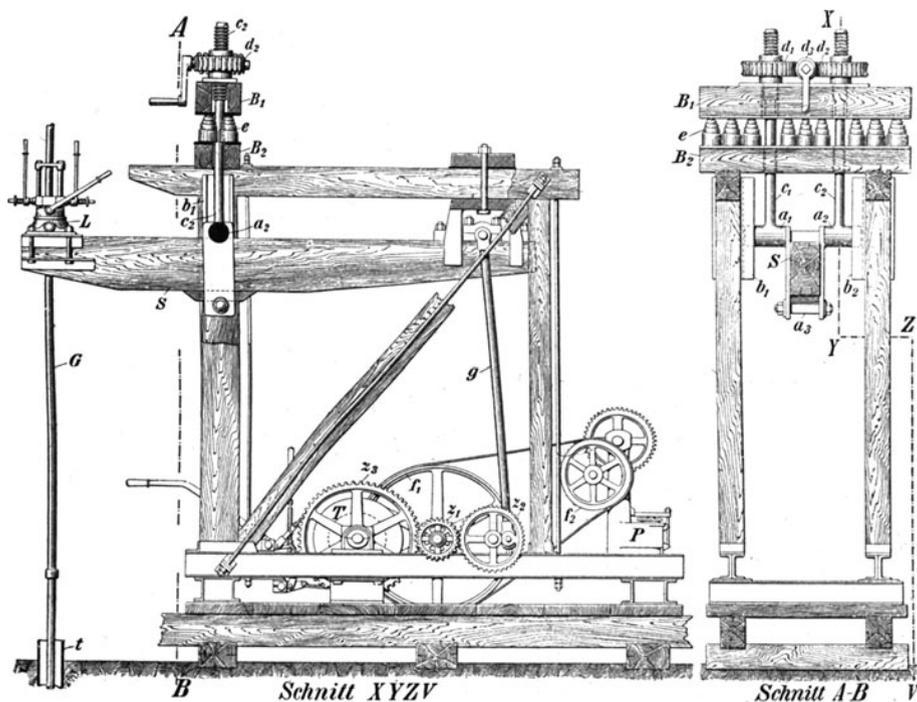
Federnd aufgehängter Bohrschwengel nach A. Raky.
